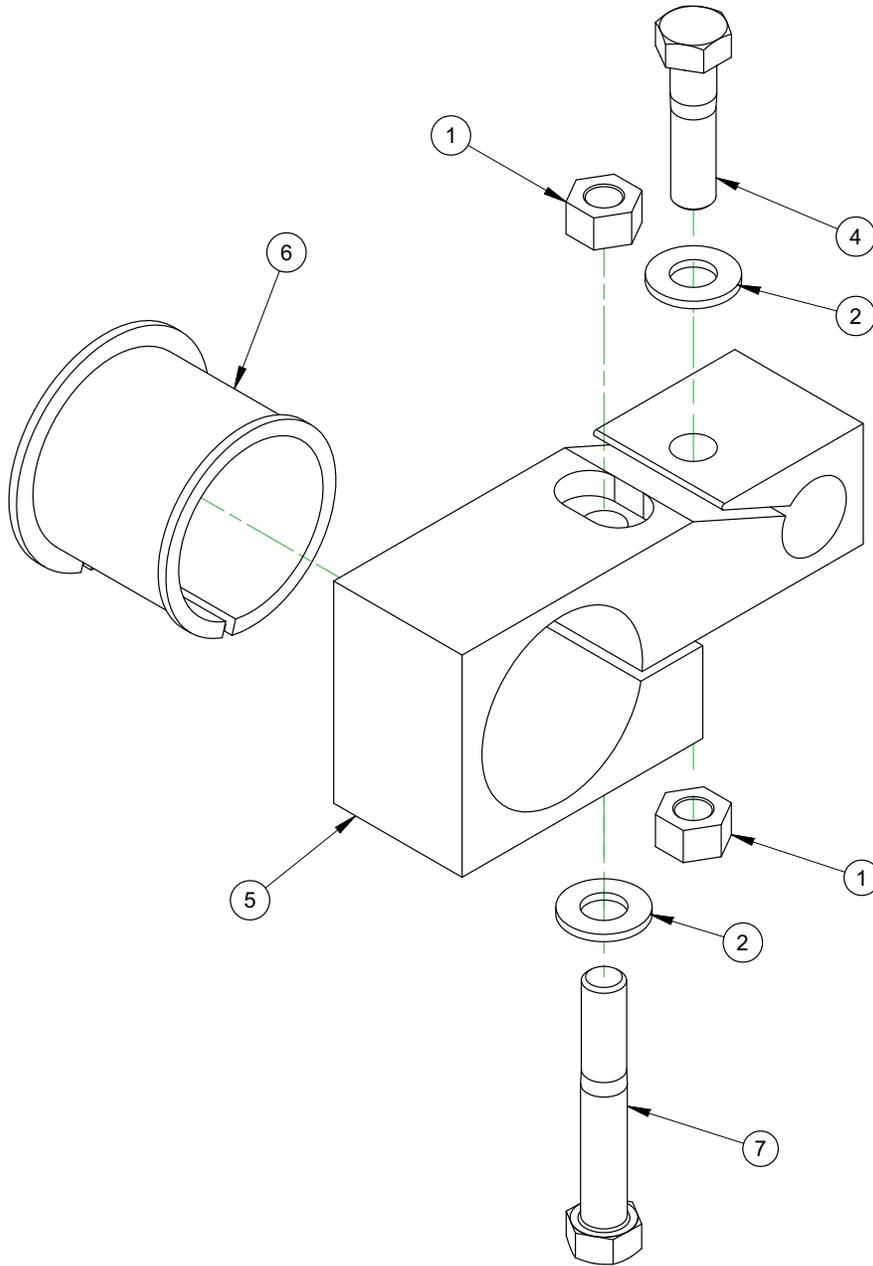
CONJUNTO DEL POSICIONADOR ESCALONADO (N/P 90590)
